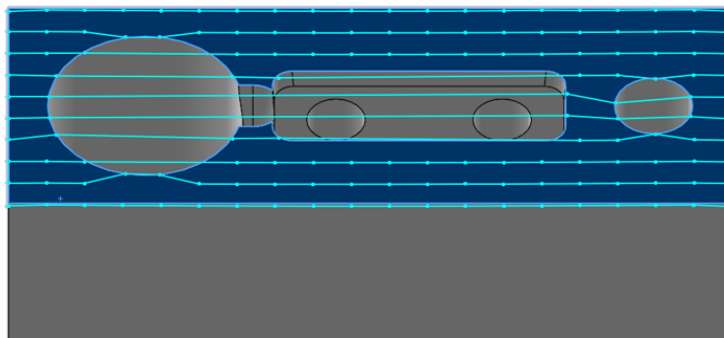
Superposició dels punts de la superfície al CAD (Font pròpia)
